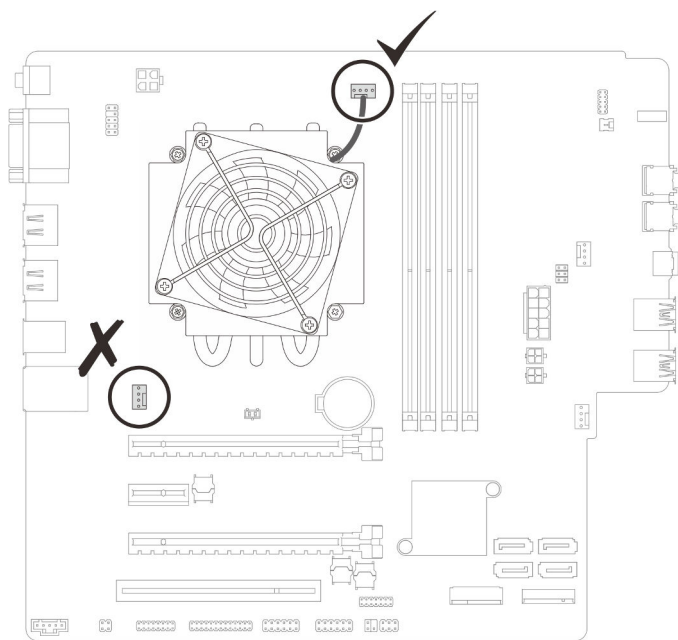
Aligner le dissipateur thermique et le module ventilateur
